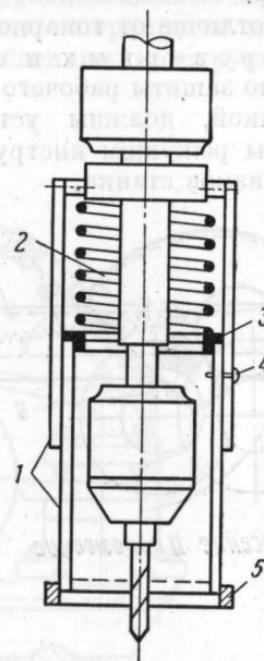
Телескопическое, прозрачное ограждение патрона и сверла сверлильного станка:
